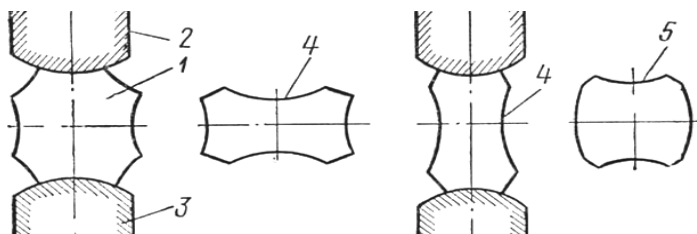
Поперечні обтискування заготовки при протягуванні бойками з випуклою робочою поверхнею [20, 78]
